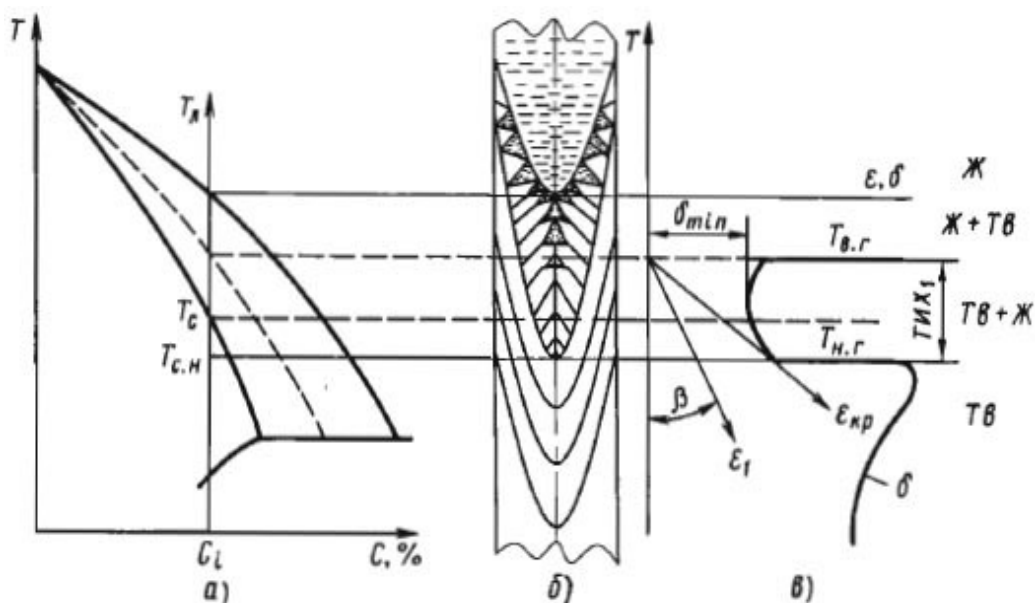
Схема процесса образования горячих трещин в сварных швах:
